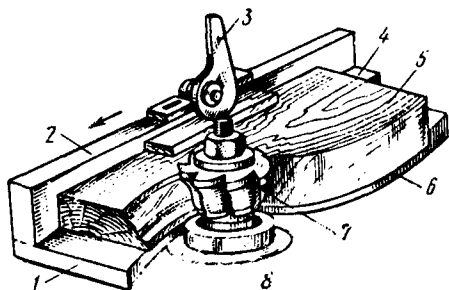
Приспособление для фрезерования криволинейных кромок:
